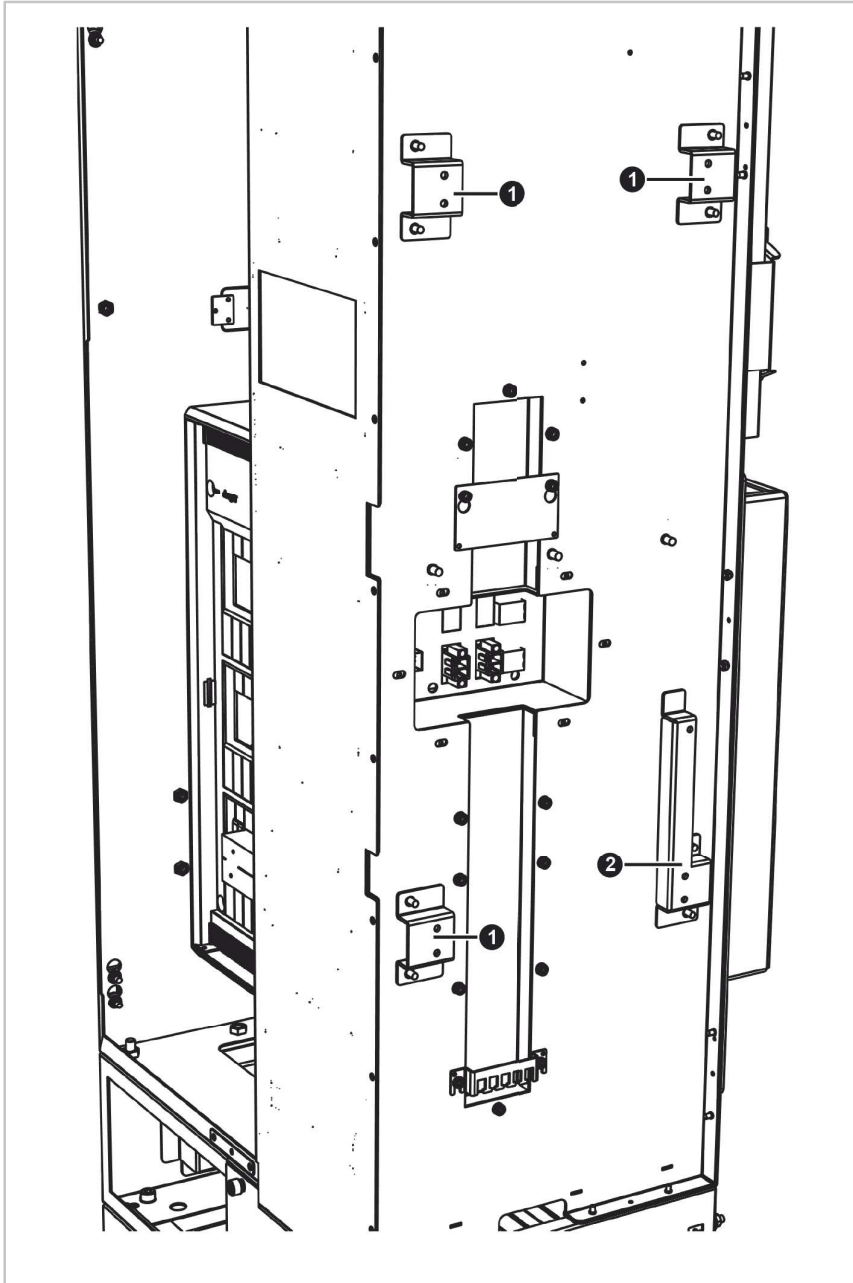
Halter zur Verbindung mit dem Batterieschrank montieren
